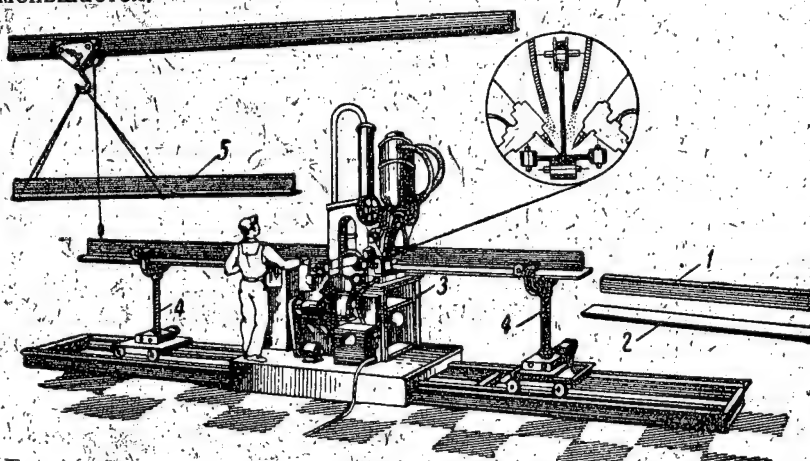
Сборка и автоматическая сварка тавровых балок на станке «СТС» (в круге — схема сборки и сварки в тавр): 1 и 2 — стенка и пояс балки, 3 — станок «СТС», 4 — винтовые подставки, 5 — готовая балка
